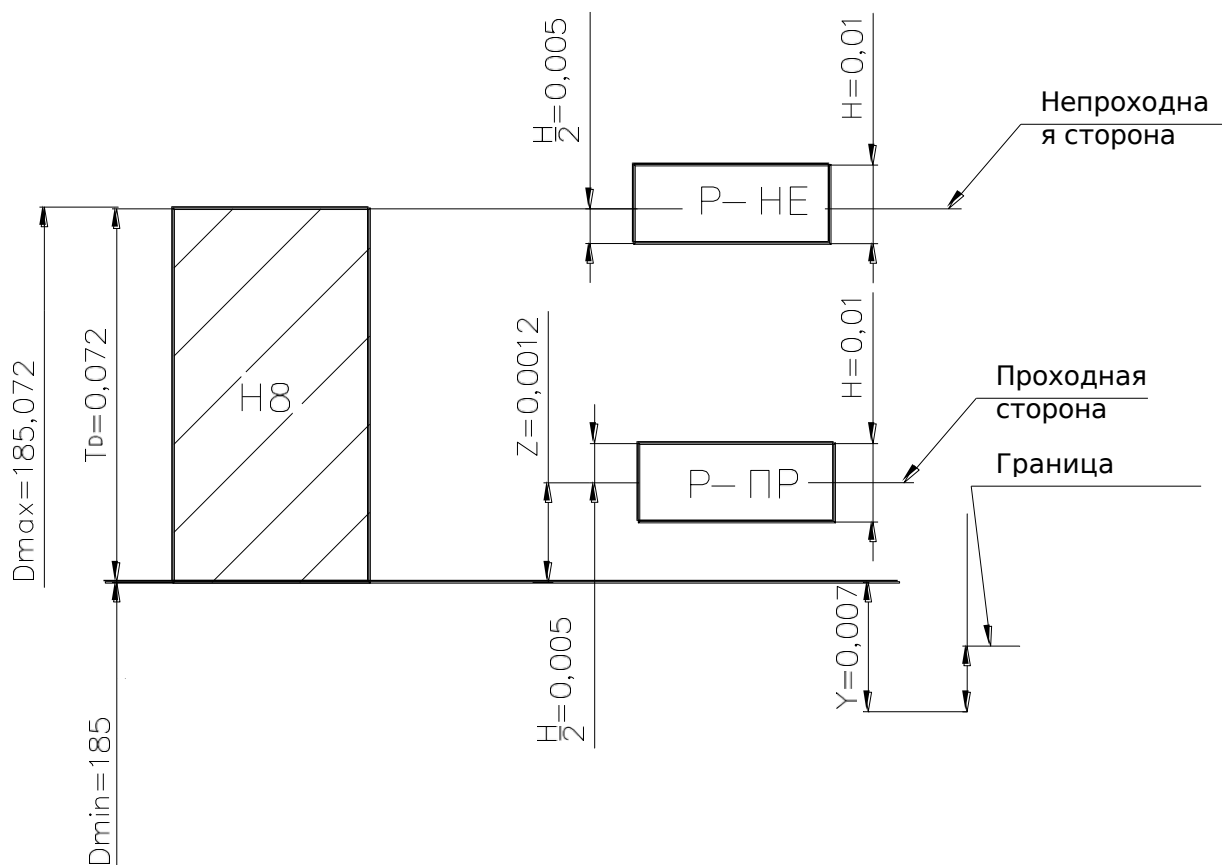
Схемы полей допусков для калибров-пробок
